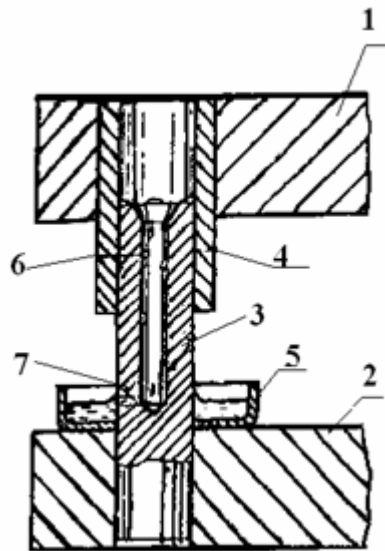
Конструкция штампового блока с самосмазывающимися колонками и втулками
